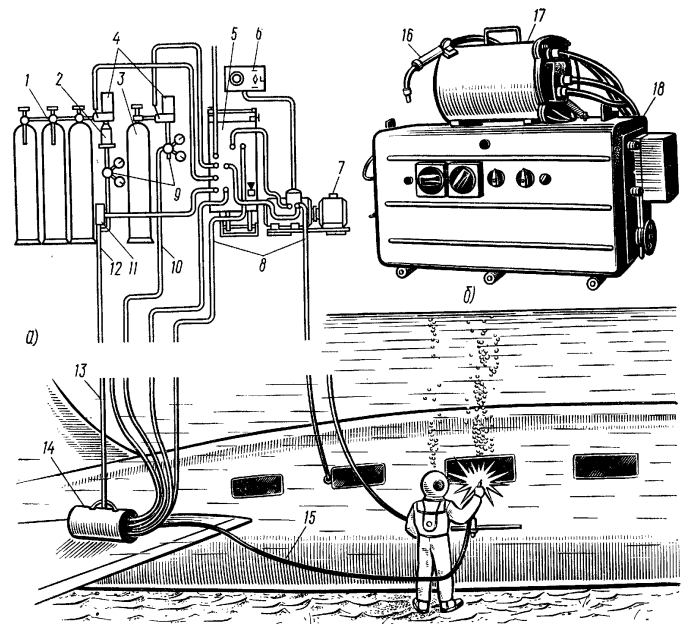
Полуавтомат типа ППСР-300-2 для подводной сварки и резки:
